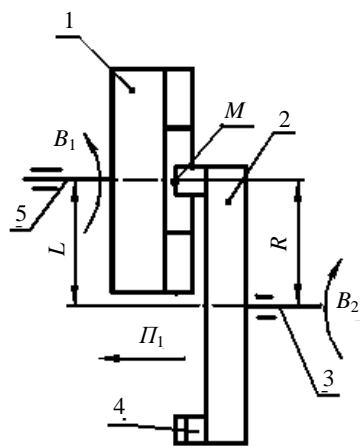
Схема кинематического формирования ТЗК резцовой головкой
